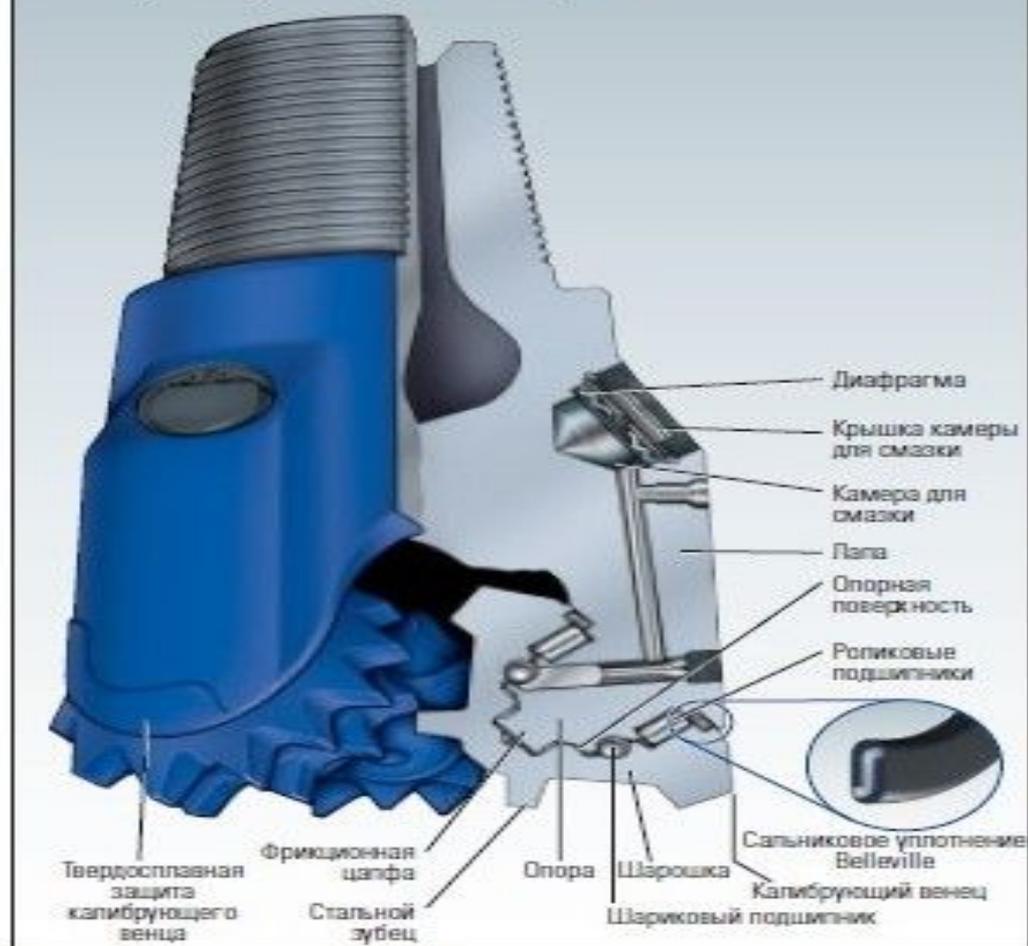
Подшипники качения. Долота с тремя шарошками, которые являются наиболее распространенными шарошечными долотами, очень мало напоминают шарошечные долота первых конструкций. Роликовые подшипники несут большую часть нагрузок, и шариковые подшипники, установленные через отверстие в опоре, удерживают шарошки на месте. Опорная поверхность и фрикционная цапфа несут осевую нагрузку и стабилизируют подшипники. Сальниковые уплотнения удерживают смазку внутри подшипников и предотвращают попадание внутрь бурового раствора и твердых частиц. Первые резиновые уплотнения были усилены внутренним металлическим кольцом или пружиной Belleville. Позднее стали использовать круглые и радиальные уплотнения из эластомера. Камеры в лапах обеспечивают смазку. В сальниках нет перепада давления, и гидростатическое давление передается через диафрагму для выравнивания давления между подшипниками и в затрубном пространстве скважины.
